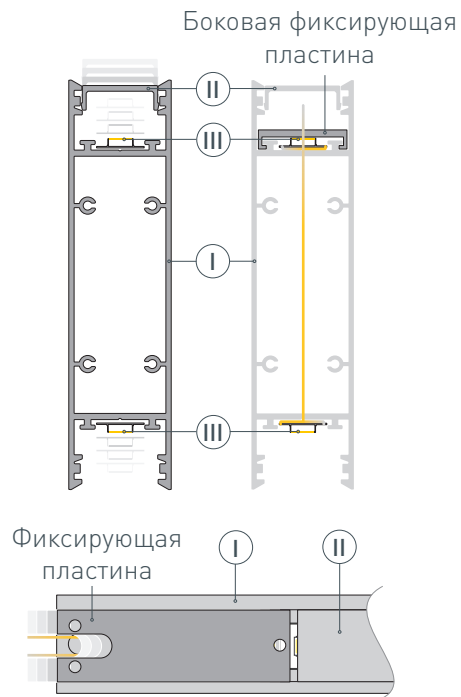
Установка боковой фиксирующей пластины на профиль I. Вид сверху
